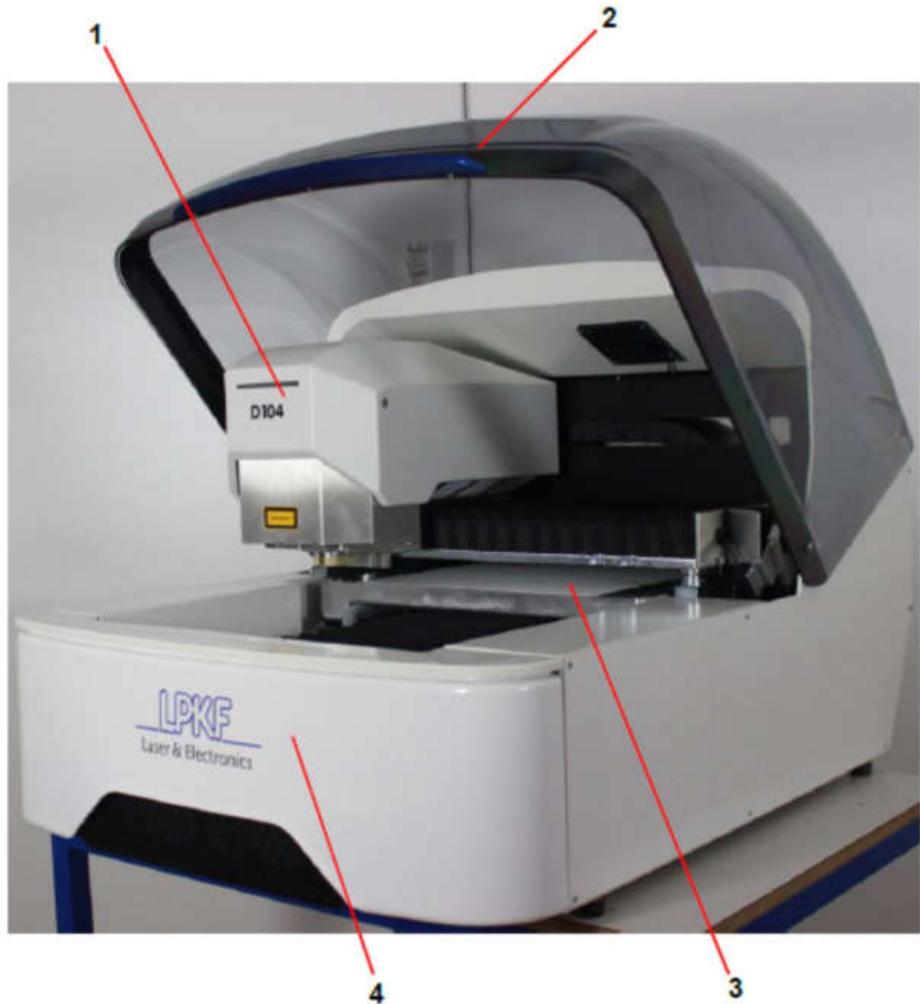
Внешний вид ProtoMat D104 (1 – обрабатывающая головка, 2 – крышка, 3 – вакуумный стол с инструментальным магазином, 4 – корпус).
